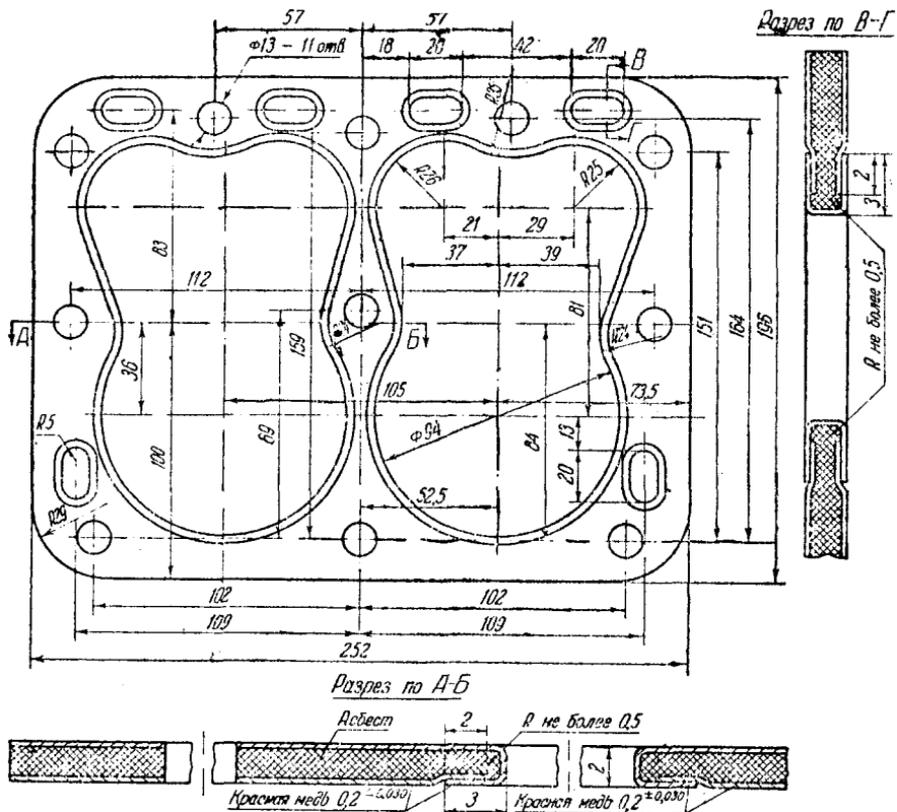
Дет. № 40243. Прокладка к головке цилиндров
